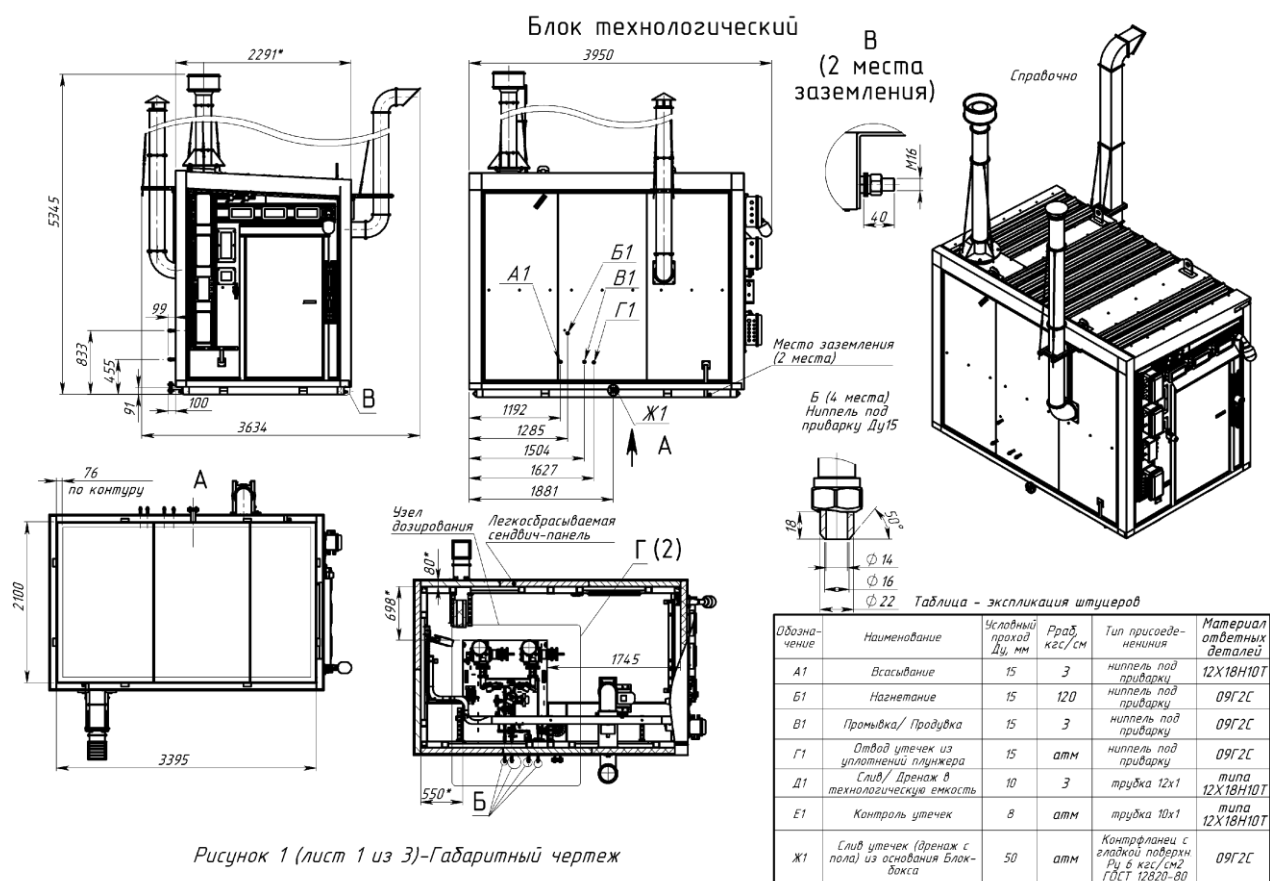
(лист 1 из 3)-Габаритный чертёж
